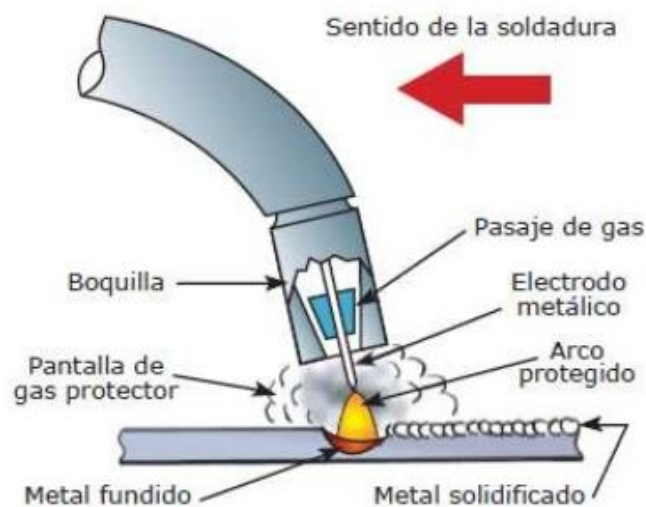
Soldadura eléctrica por arco bajo protección de gas con alimentación continua de electrodo sólido (GMAW) [17].
